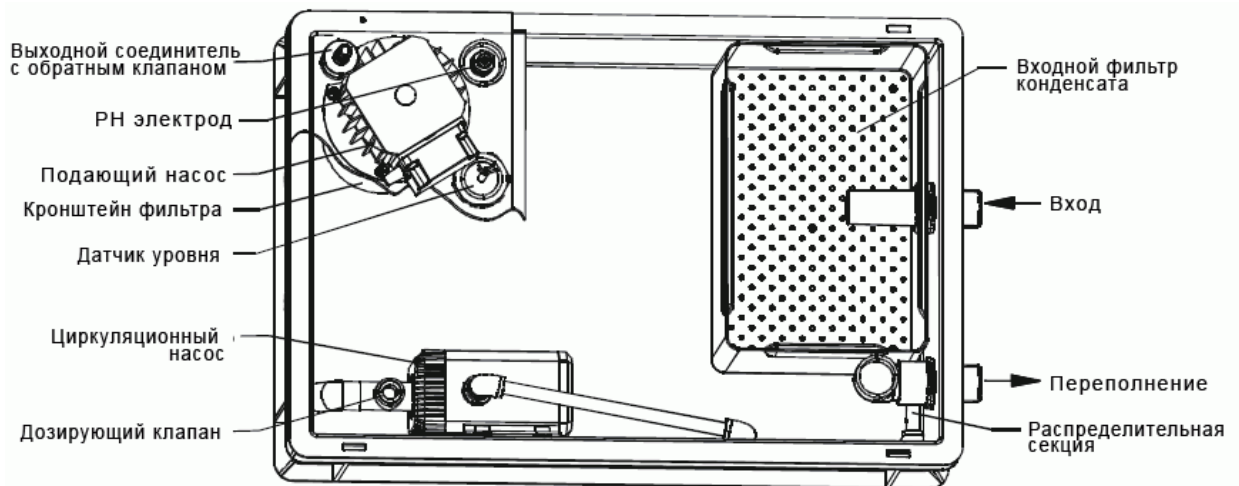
Внутренний вид узла нейтрализатора, частично с крышкой
